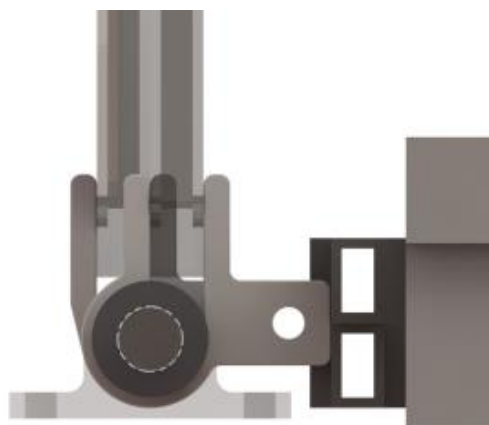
Vista axial del conjunto deslizante del eje guía. (Fuente: Propia)
